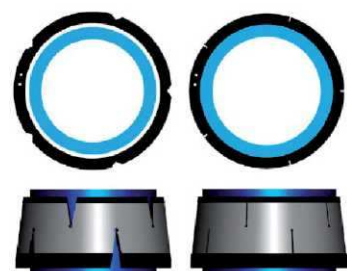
Принцип работы конической сварочной манжеты: разрывы обеспечивают возможность эластичного уменьшения диаметра при заполнении манжетой зазора между трубой и муфтой.
